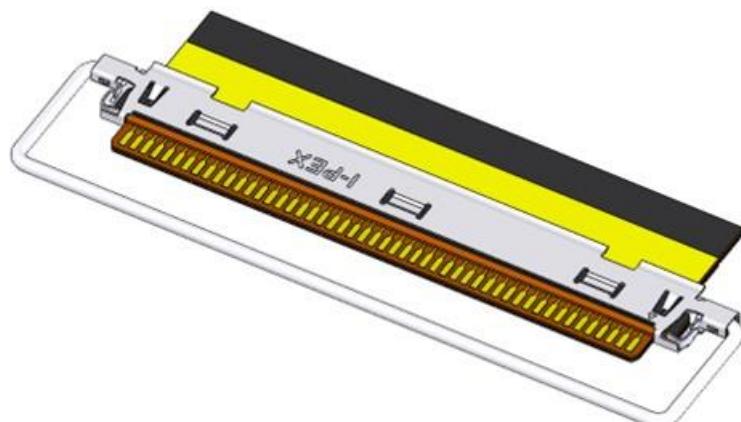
CABLINE-CAL IIF Shell Assembly with FPC
